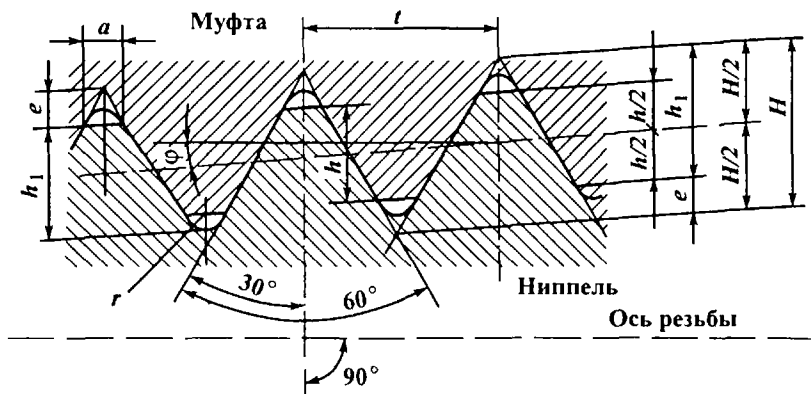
Профиль замковой и метрической конической резьбы
